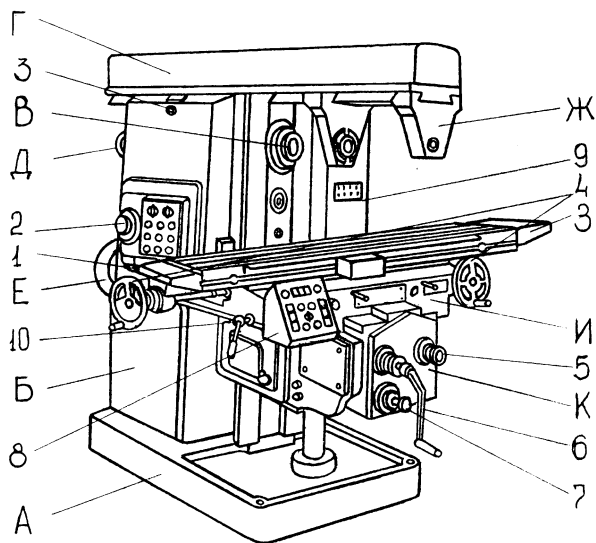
Общий вид горизонтального консольно-фрезерного станка 6Т82Г-1.
